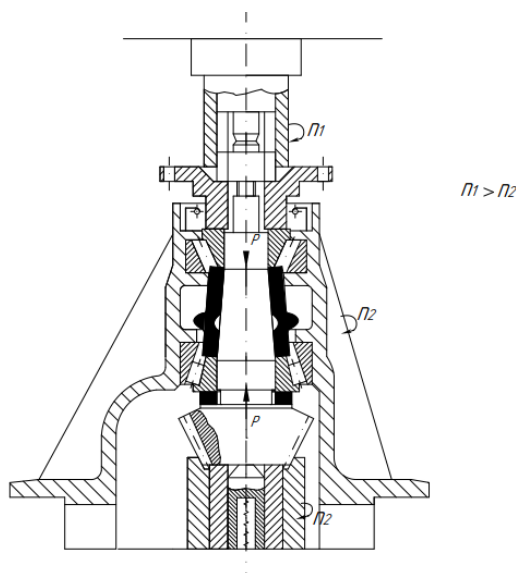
Схема установки ведущей шестерни в картере на стенде регулировки преднатяга подшипников:
